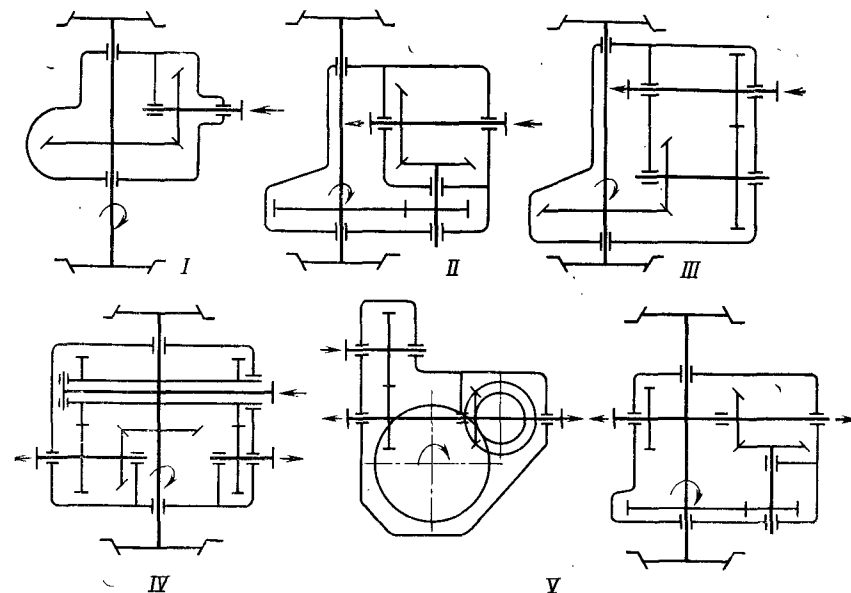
Кинематические схемы осевых редукторов тепловозов с гидропередачей: I — одноступенчатый; II — двухступенчатый коническо-цилиндрический; III — двухступенчатый цилиндрическо-конический; IV — двухступенчатый раздаточный; V — трехступенчатый раздаточный
